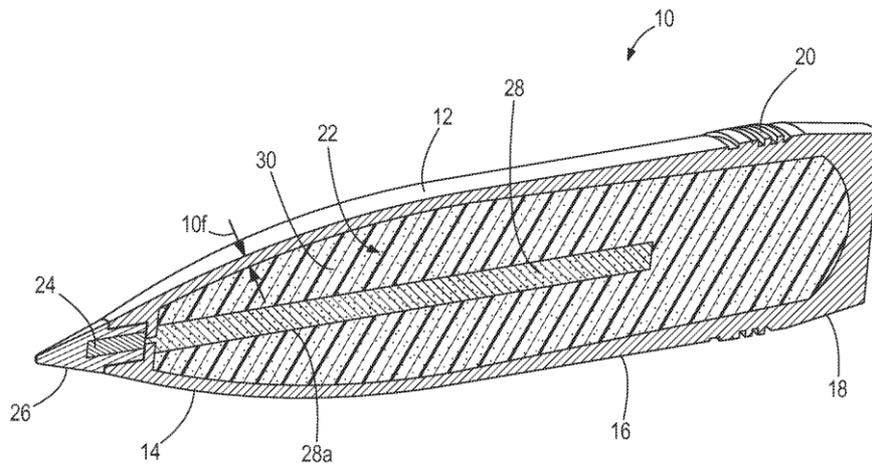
Projectil extintor de explosión, vista interior. Fuente:[17]
